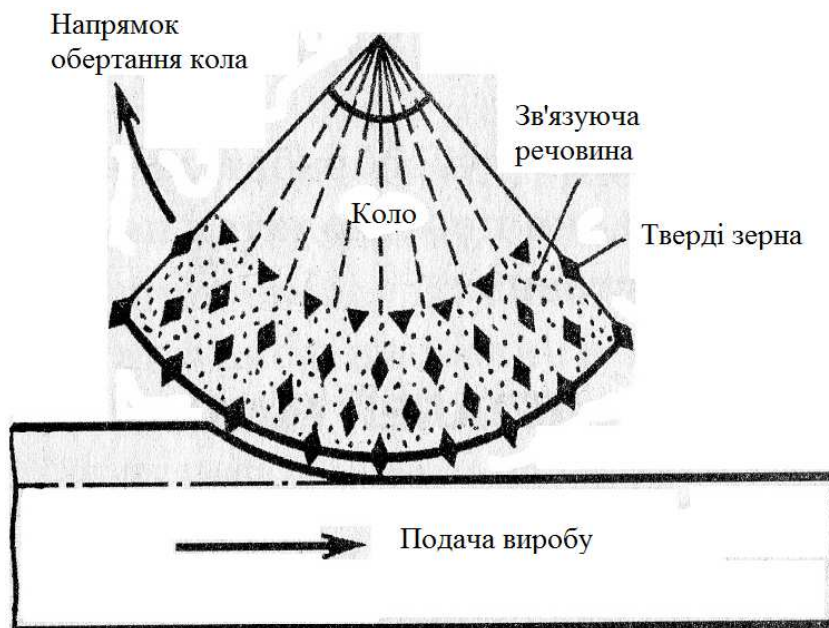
Процес обробки заготовки шліфувальним кругом
